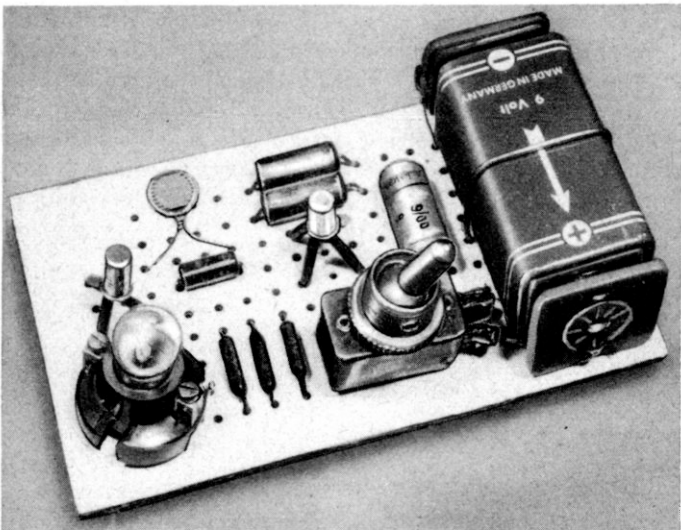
Aufbaubeispiel des Dämmerungsschalters
